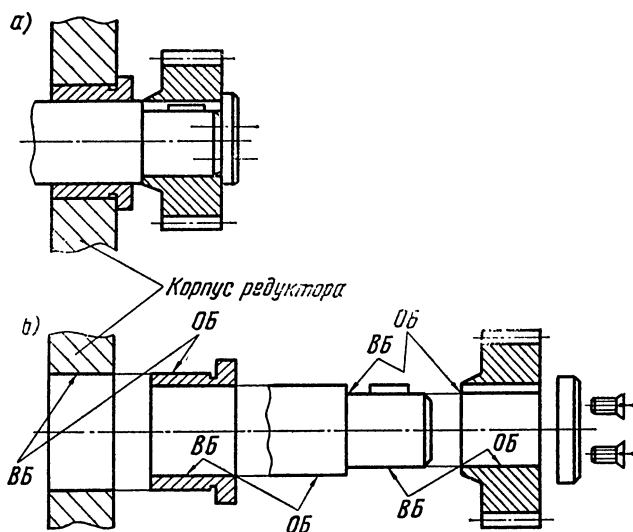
Базы сопрягаемых деталей: а — собранный узел; б — элементы (детали); ОБ — основная база; ВБ — вспомогательная база
